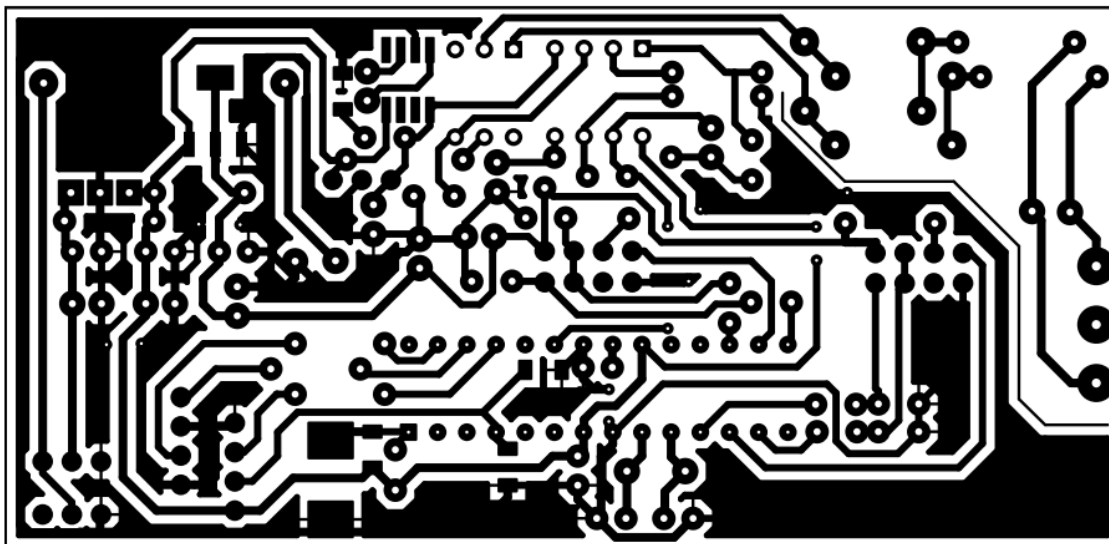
Plantilla PCB para el módulo principal.
